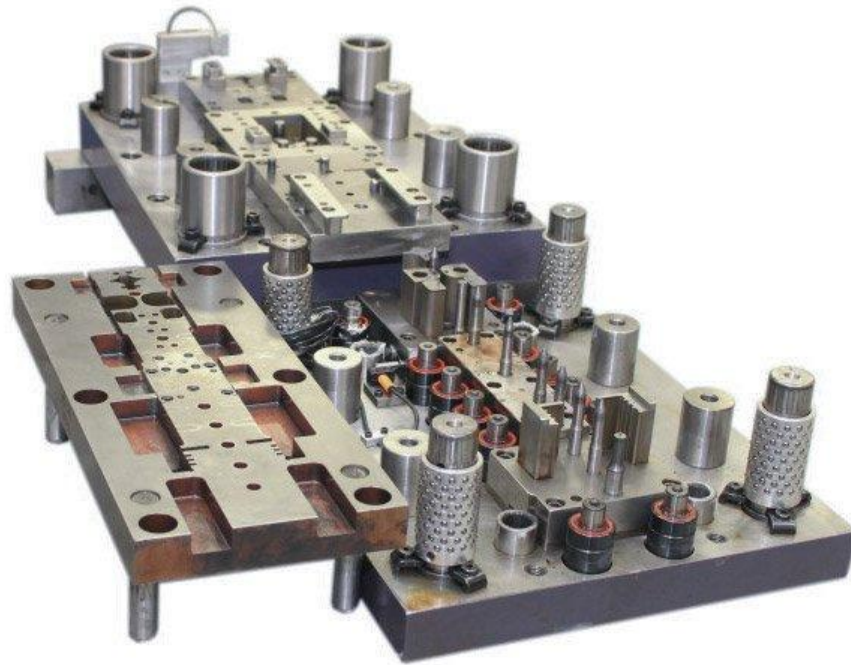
Moule industriel en acier trempé fabriqué par usinage CN multi-axes [27].
